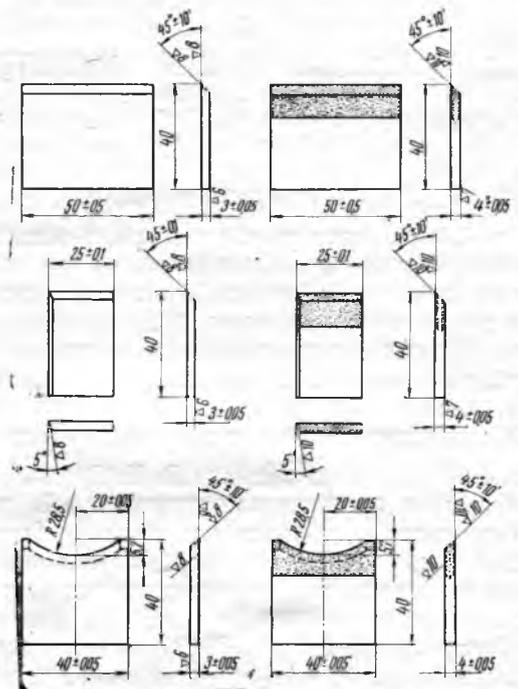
Ножи к цилиндрическим сборным фрезам (слева — из стали Р9, справа — армированные твердым сплавом ВК10)
